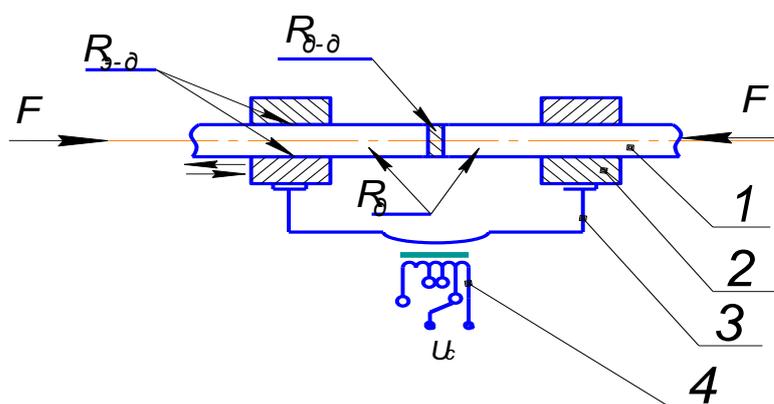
Схема процесса контактной стыковой сварки.
